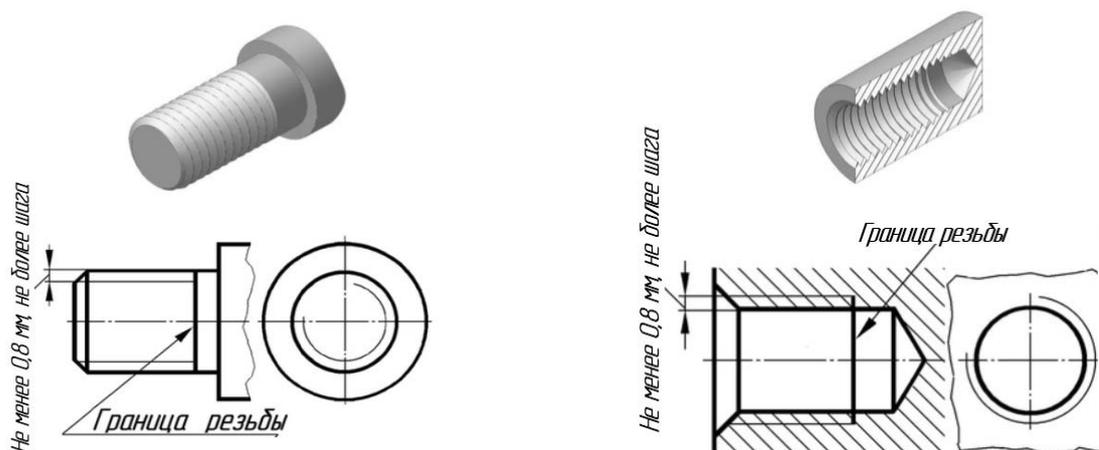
Изображение резьбы на цилиндрических поверхностях
